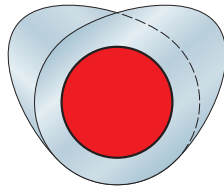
Положение кулачков первого цилиндра при укладке распределительного вала в опоры головки блока цилиндров
